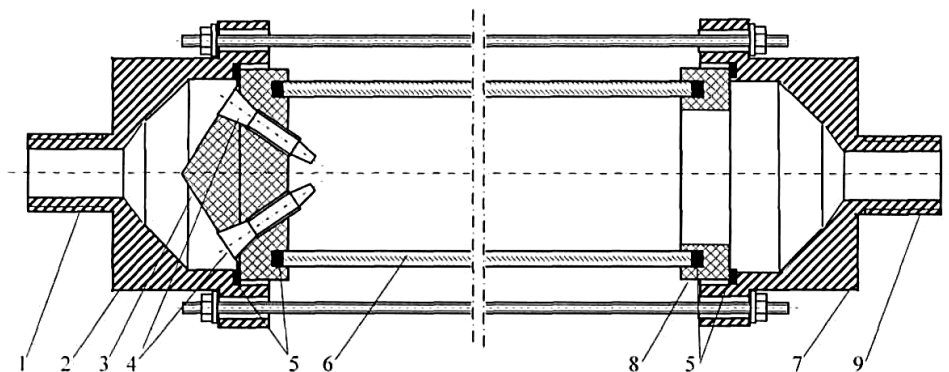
Схема гідродинамічного струминного кавітатора: 1 - патрубок подачі води; 2 – обойма; 3 – вставка; 4 – сопло; 5 – ущільнення; 6 – корпус; 7 – обойма; 8 - вставка; 9 - патрубок відведення води
